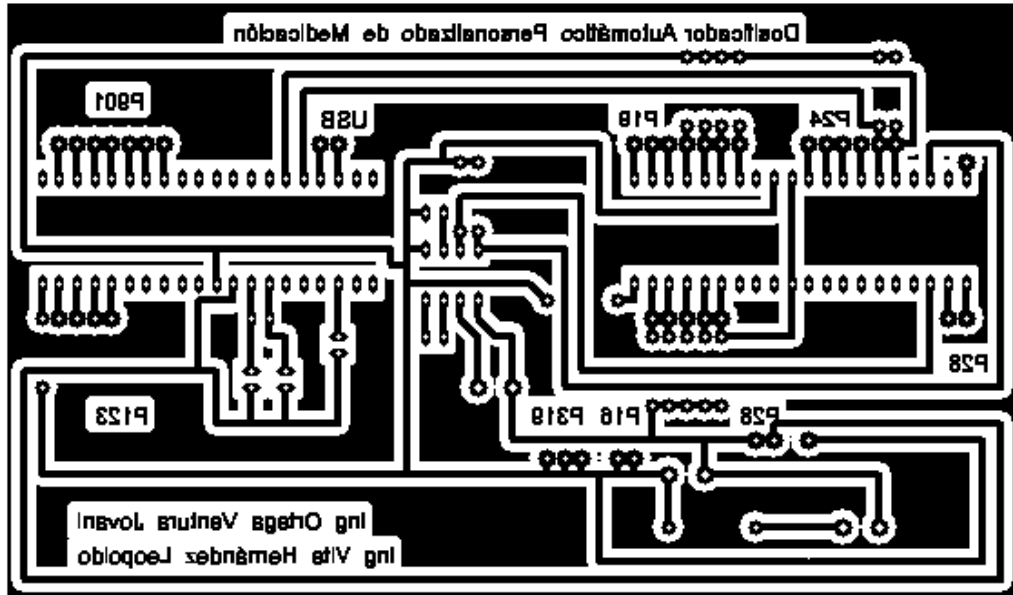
Diseño del PCB listo para imprimir en el papel ilustración (cucho).
